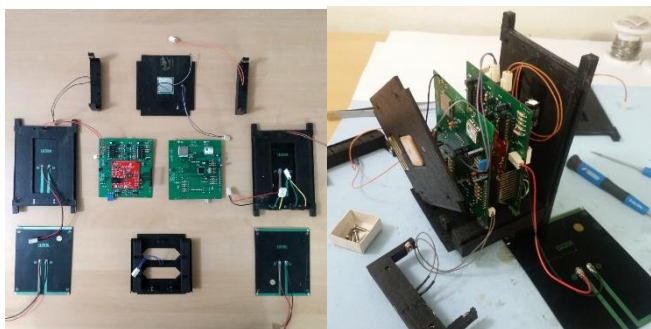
Esq. peças separadas do frame e placas PCB. Dir. inserção das placas no frame e conexão com as placas laterais
